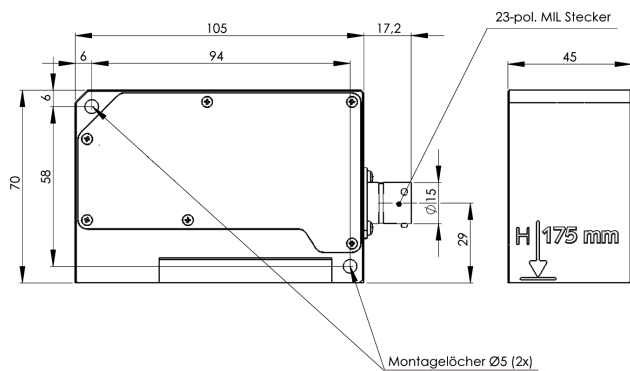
Abmessungen Correvit S-175 Racing Sensor
